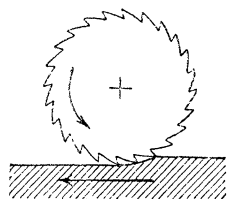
Деталь движется справа налево и поступательно, а резец (фреза) вращается.
